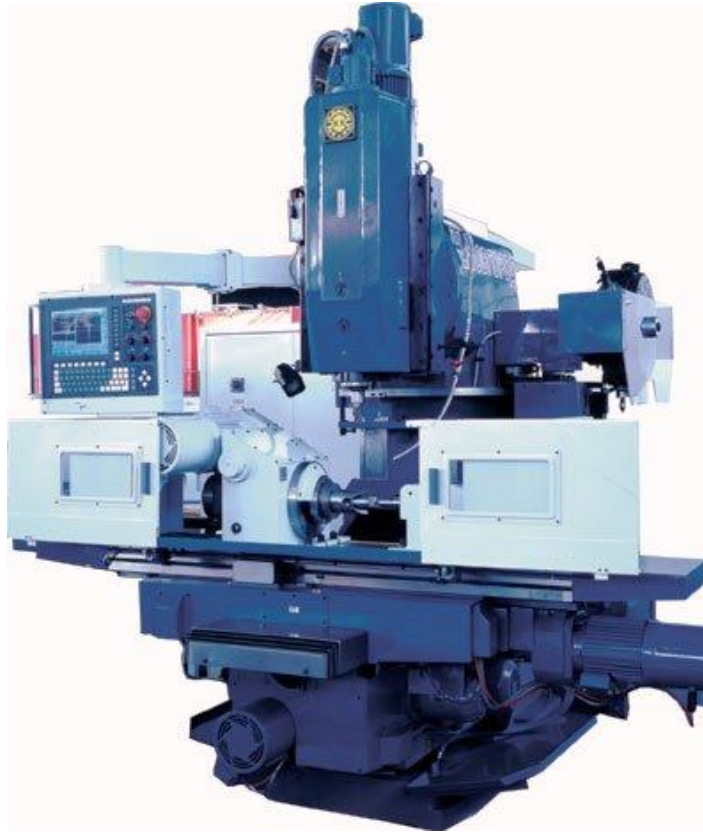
Вертикальний консольний багатоінструментальний фрезерний верстат з ЧПК моделі ГФ2171С5
